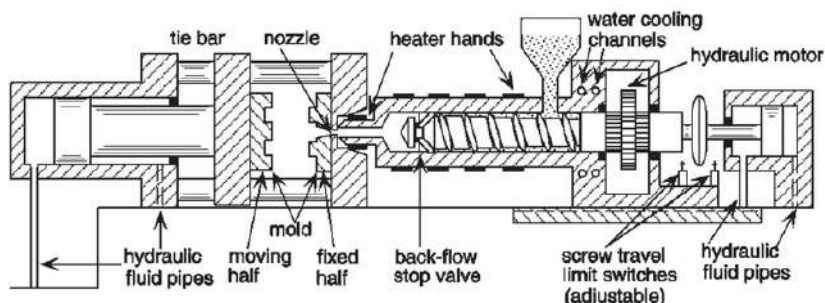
Representação de máquina de moldagem por injeção (Fried, 2014)
